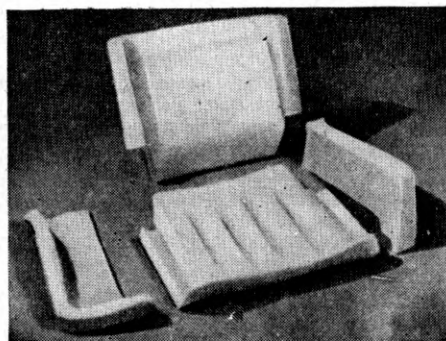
Комплект готовых литых деталей из полиуретанового пенопласта для кресла
